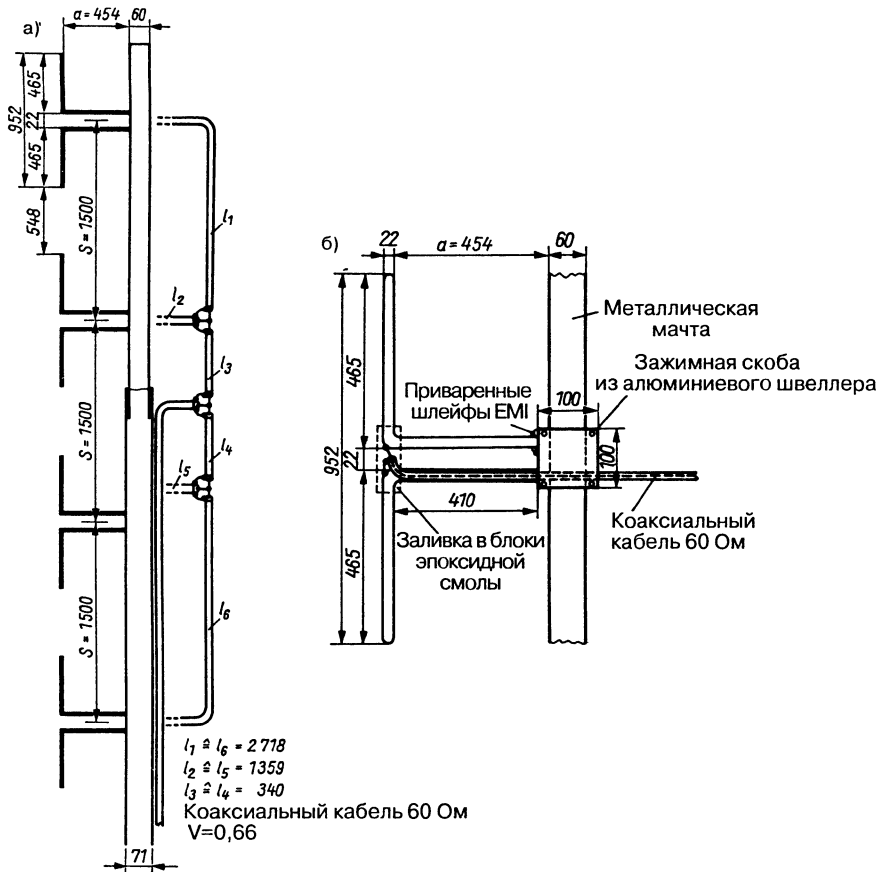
Вертикальный вибраторный ряд из четырех поэтажно расположенных полуволновых вибраторов: а – устройство и схема возбуждения; б – детали вибратора со шлейфом ЕМИ
